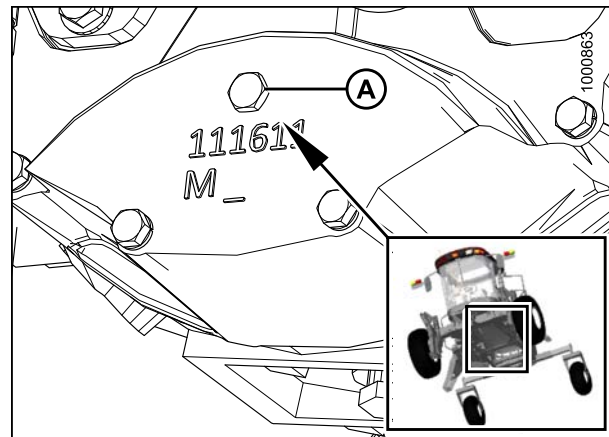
Пробка отверстия для контроля масла главного редуктора
